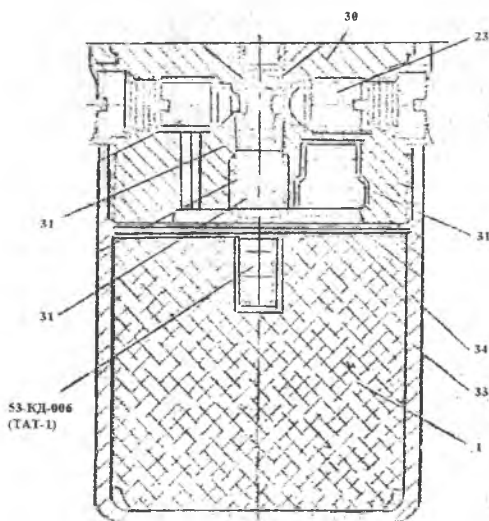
Замедлительный и детонирующий узлы: 1- детонатор; 23- установочный винт; 31-втулки замедлителя; 32- пороховые цилиндрики; 33- стакан детонатора; 34- прокладка
